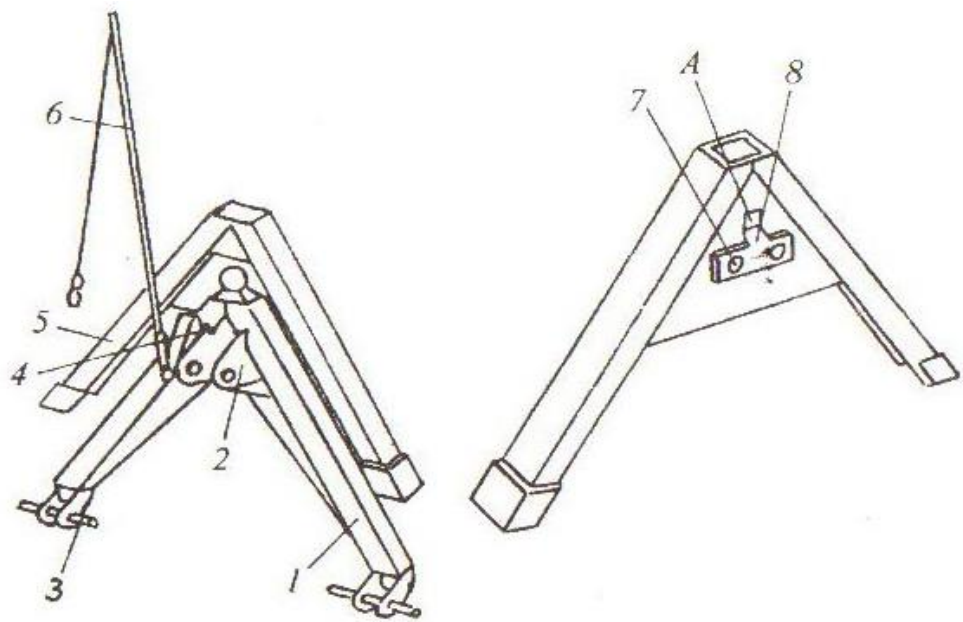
Зовнішній вигляд конструкції автоматичної зчіпки: 1 – рамка; 2 – планка; 3 – пальці; 4 – стопорна собачка; 5 – замок; 6 – рукоятка; 7 – ексцентрик; 8 – упор «собачки»; А – паз для «собачки» рамки.
